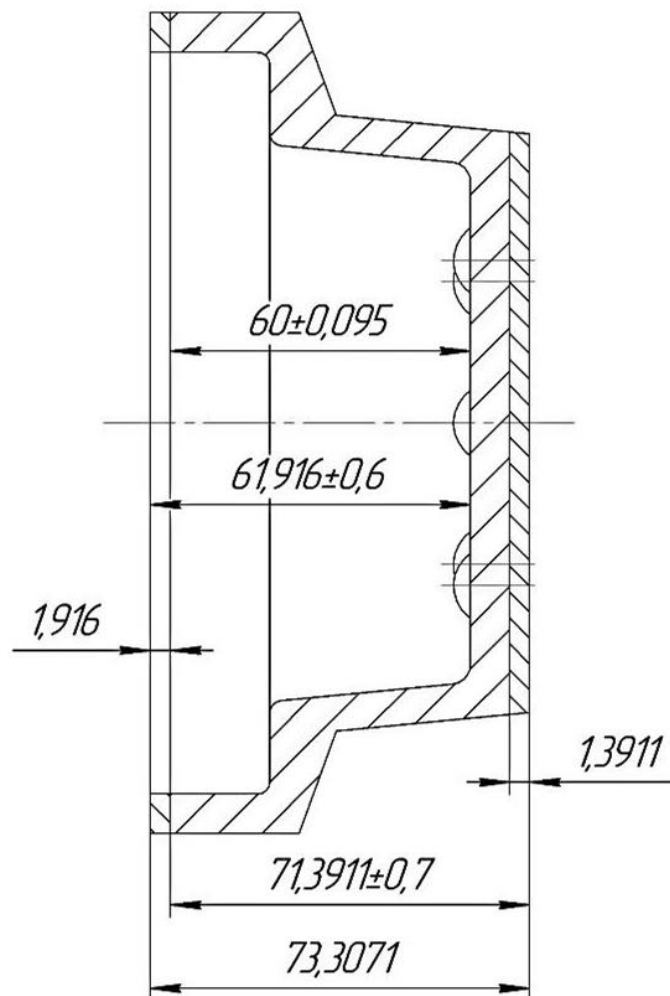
Ескіз заготовки з врахованими припусками та допусками.
